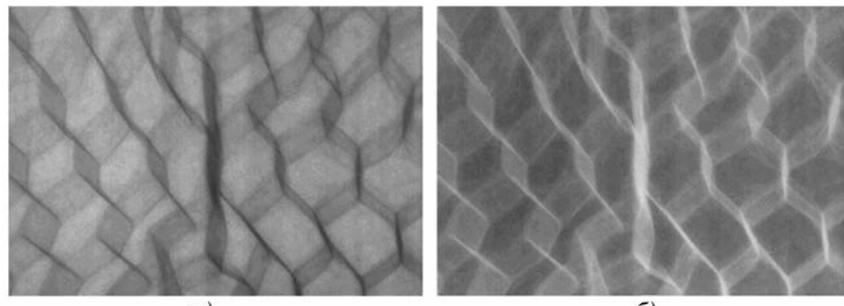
Цифровые изображения дефектного участка сотовой конструкции закрылка крыла самолета, полученные с применением миниатюрного преобразователя типа S10811-11: а – позитив; б – негатив
